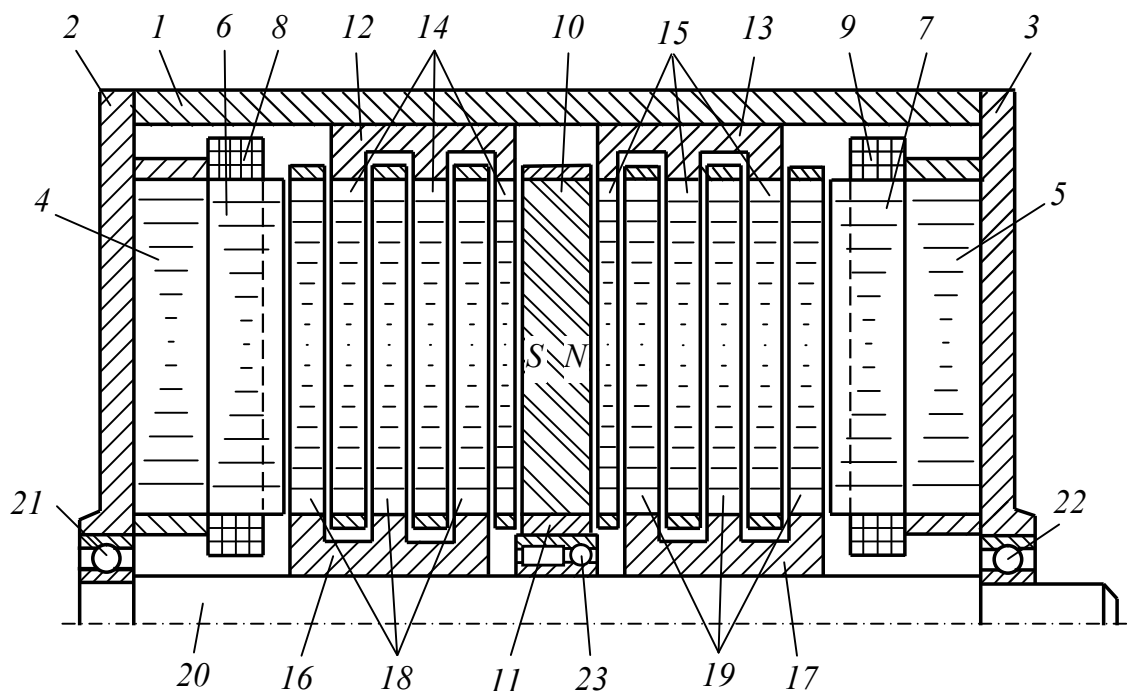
Синхронный электродвигатель с двумя обмотками: 1 – корпус; 2, 3 – подшипниковые щиты; 4, 5 – кольца пакета статора; 6, 7 – зубцы; 8, 9 – катушки; 10 – постоянный магнит; 11 – втулка ротора быстрого вращения; 12, 13 – втулки статора; 14, 15 – диски статора; 16, 17 – втулки ротора медленного вращения; 18, 19 – диски ротора медленного вращения; 20 – вал; 21, 22 – подшипники ротора медленного вращения; 23 – подшипник ротора быстрого вращения
